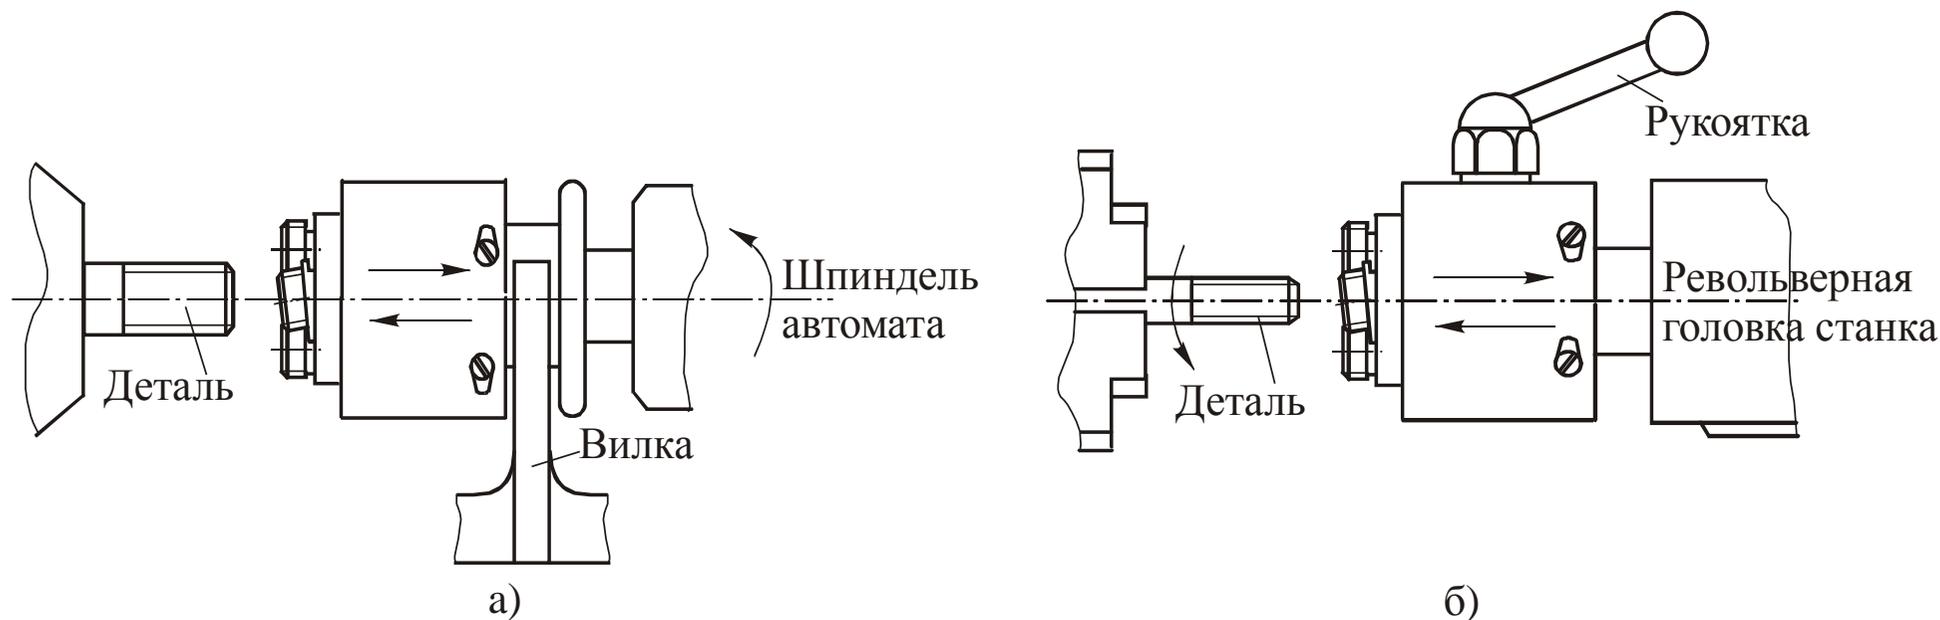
Конструкции резьбонарезных самооткрывающихся головок:
